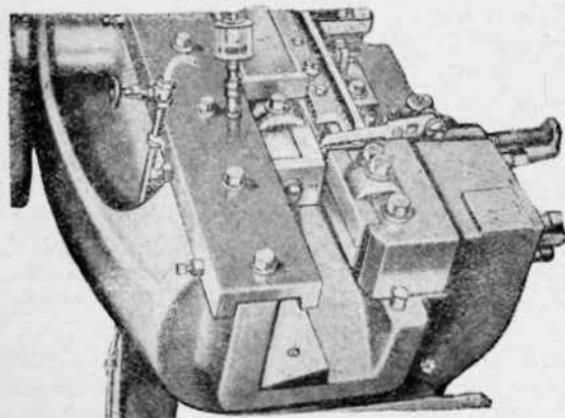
Шаровые опоры для держателя неподвижной плашки.
